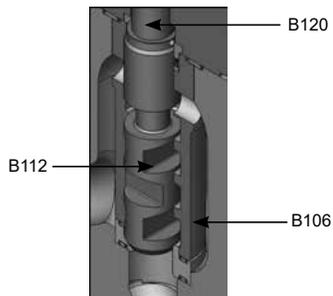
Направляющая поверхность заглушки, втулки и штока
